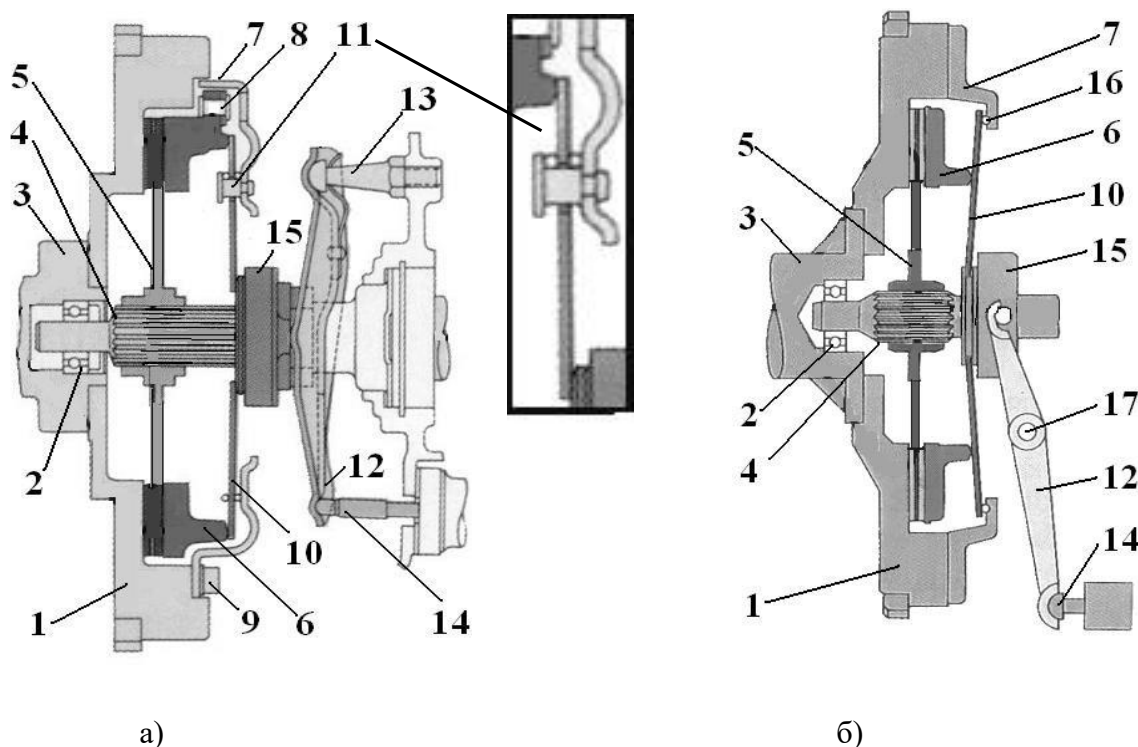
Схема однодискового постоянно включенного сцепления с центральной диафрагменной пружиной: а – установленной выпуклостью к кожуху передач, б – установленной выпуклостью к двигателю; 1 – маховик двигателя, 2 – передний подшипник первичного вала коробки передач, 3 – фланец коленчатого вала, 4 – первичный вал коробки передач, 5 – ведомый диск, 6 – нажимной диск, 7 – кожух сцепления, 8 – заклепки крепления упругих соединительных пластин к нажимному диску, 9 – болты крепления кожуха сцепления к маховику, 10 – диафрагменная пружина, 11 – узел крепления диафрагменной пружины к кожуху сцепления, 12 – рычаг привода муфты выключения сцепления, 13 – опорный болт, 14 – шток, 15 – выжимной подшипник.
